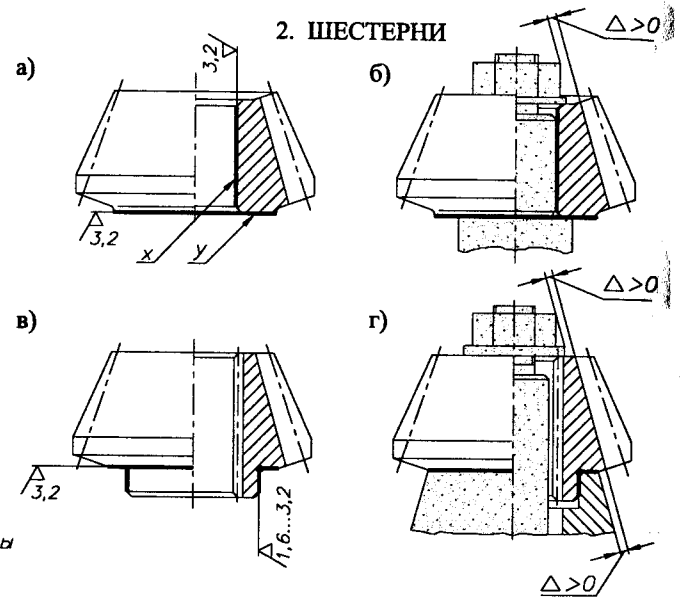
Установочные базы для нарезания зубьев на шестернях
